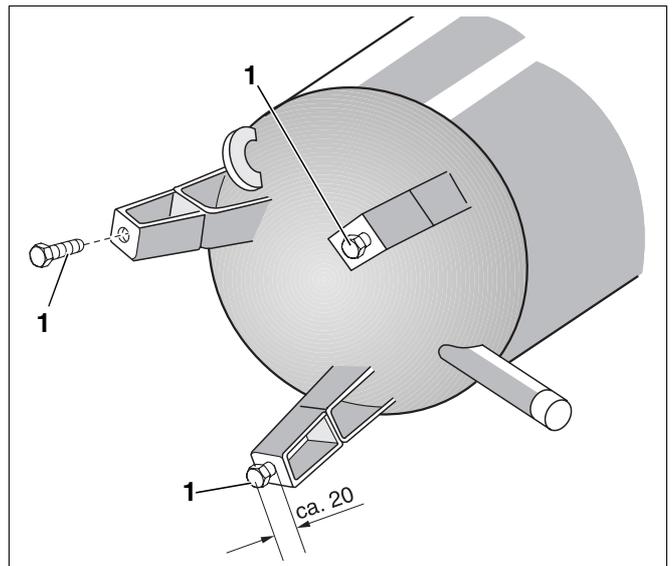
Nutzung der Befestigungsschrauben als Fußschrauben (Prinzipabbildung)
